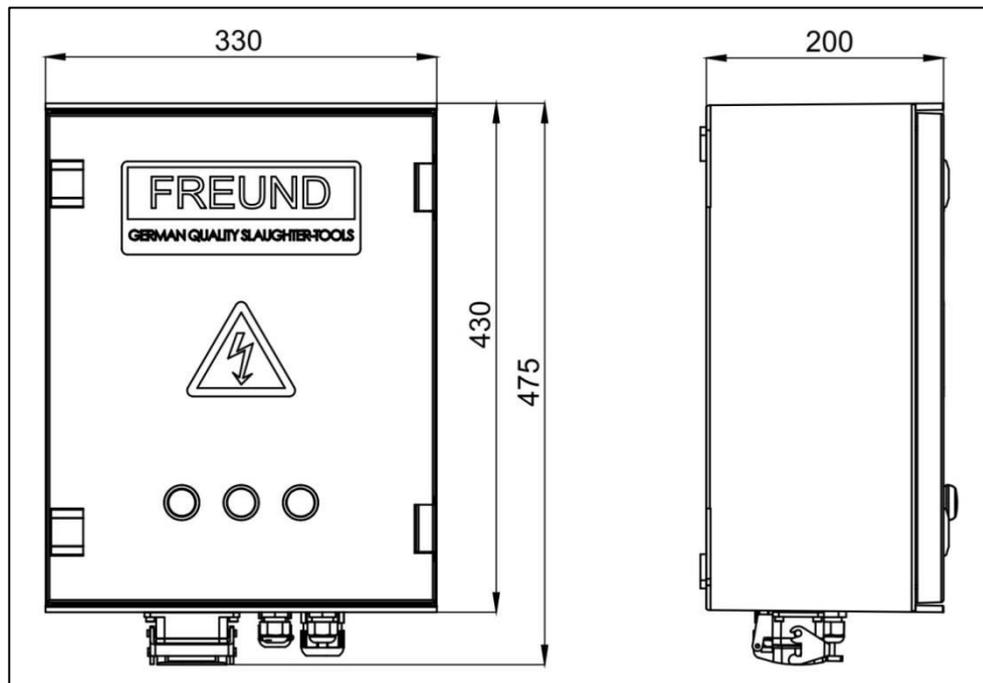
Dimensiones del dispositivo interruptor (datos en mm)
